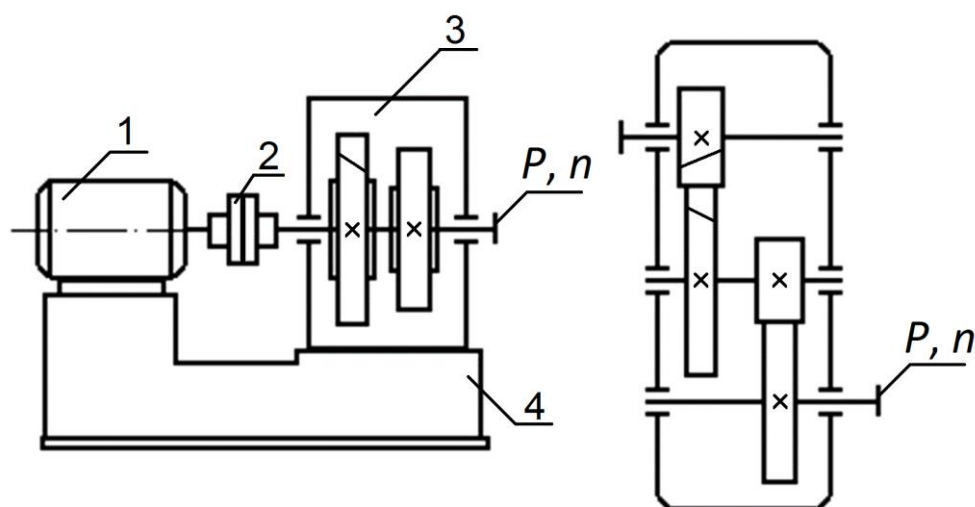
Привод бетономешалки: 1 – электродвигатель; 2 – упругая муфта; 3 – цилиндрический двухступенчатый редуктор; 4 – литая плита
